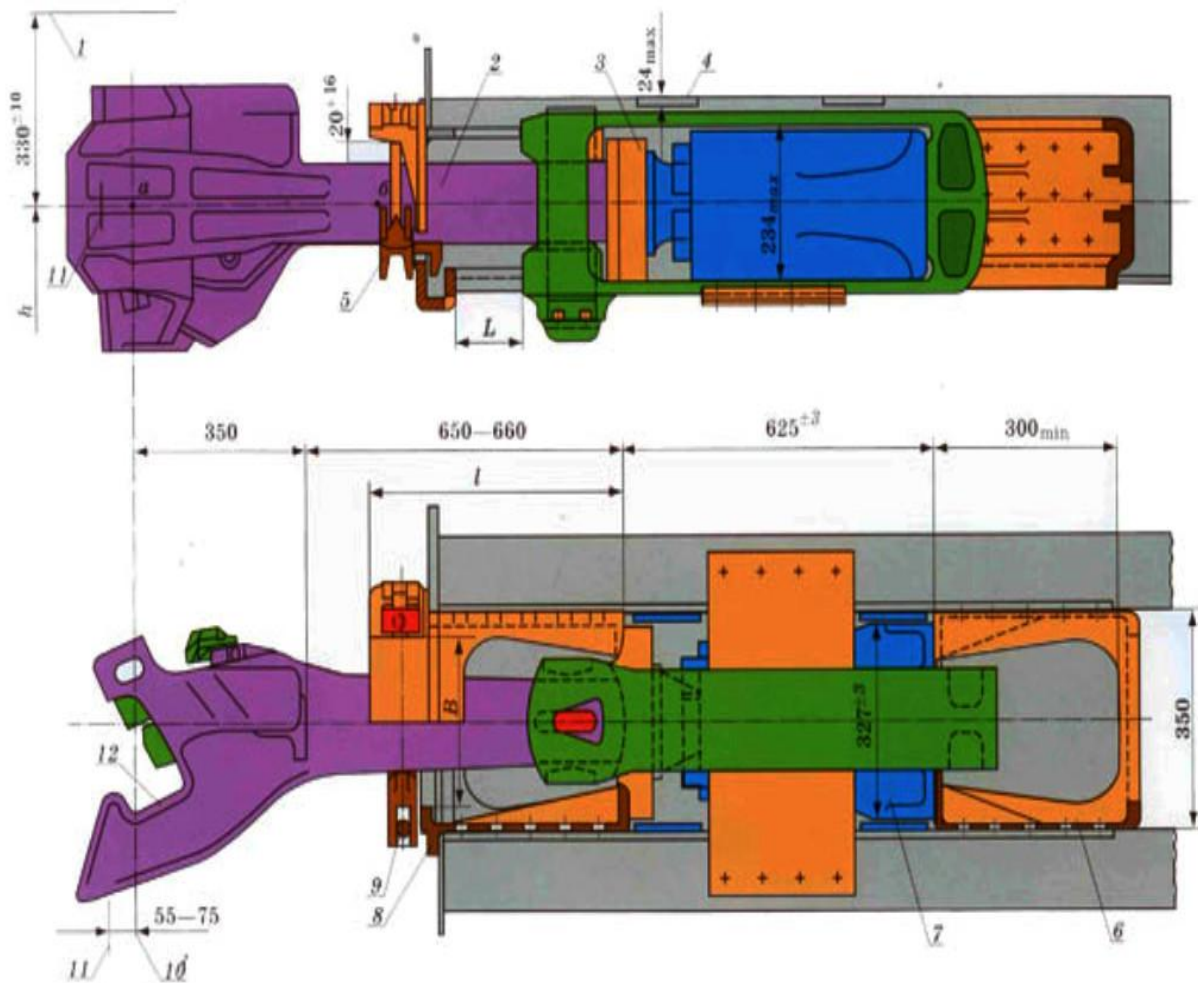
Схема стандартного ударно-тягового пристрою
